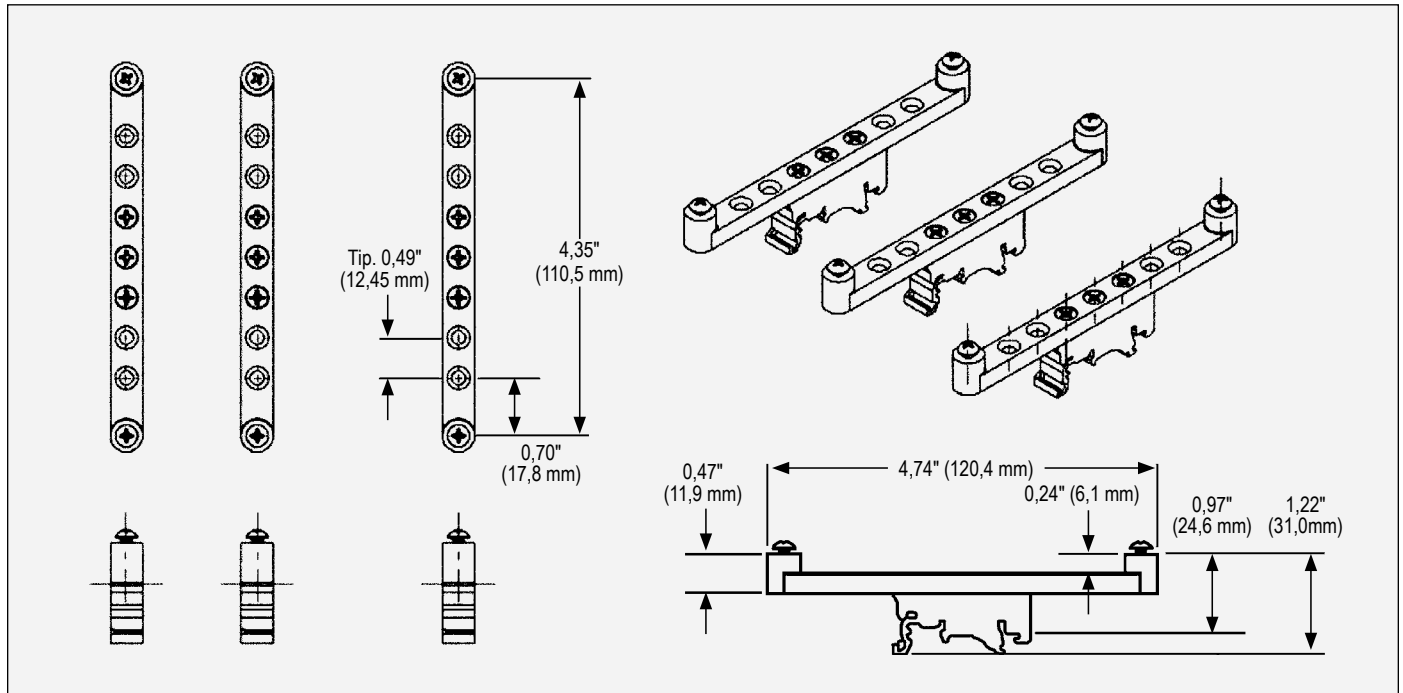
Dimensioni kit di fissaggio a guida DIN scheda MIO/DIO
